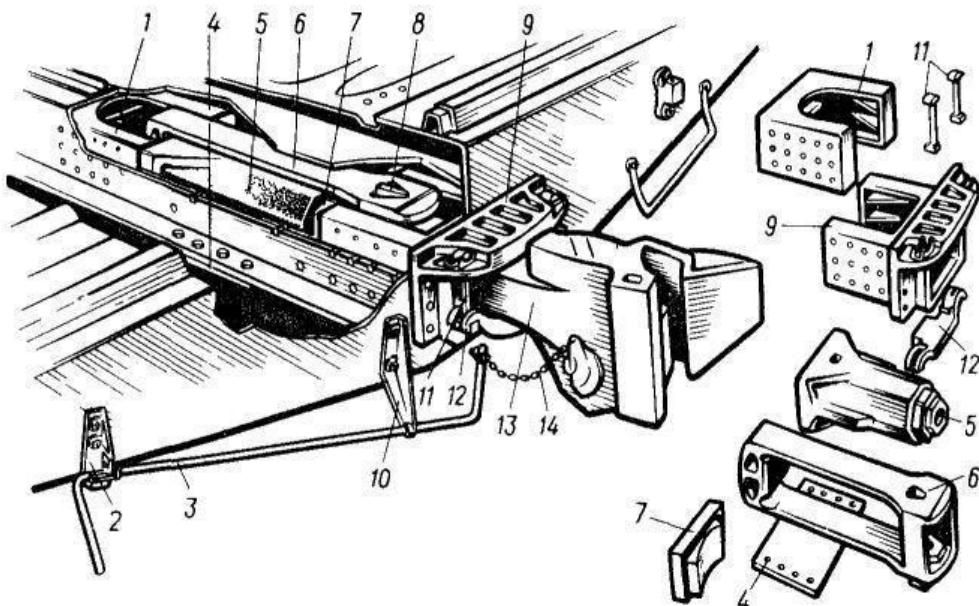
Автосцепное устройство вагонного типа и его детали
